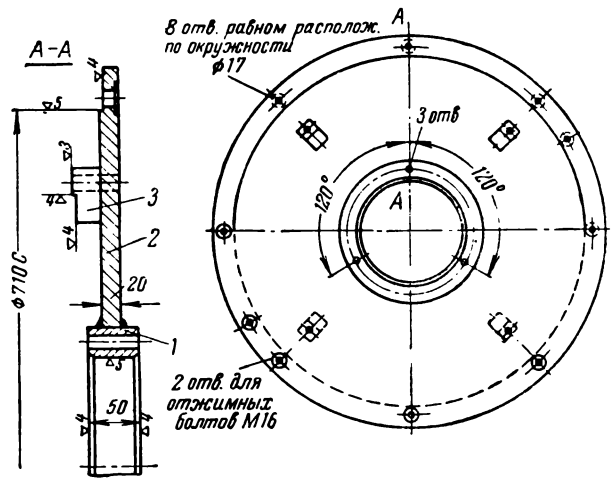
Сварной щит машины серии П-100.
